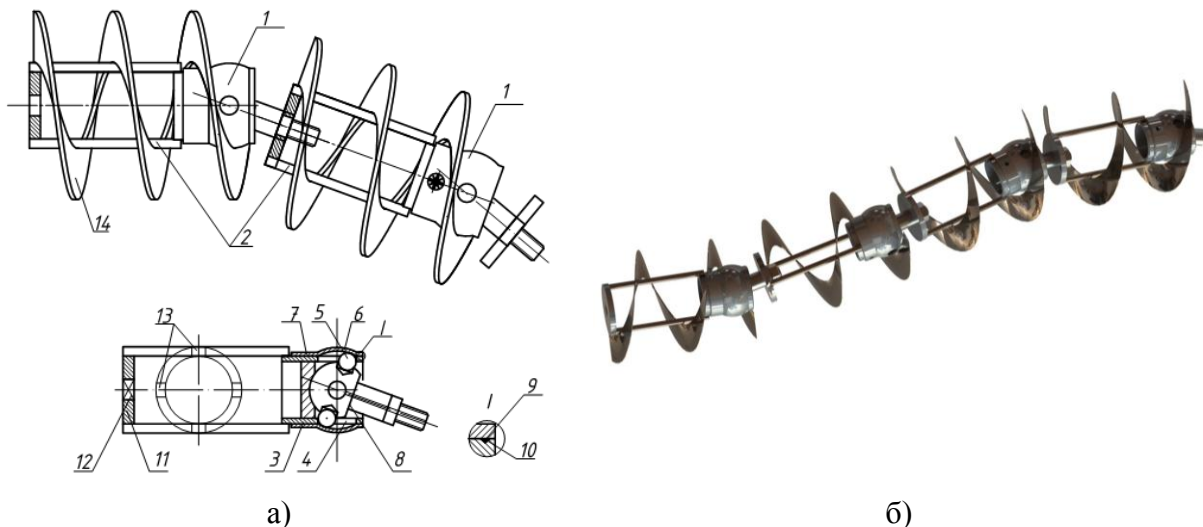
Гвинтовий шарнірно-секційний робочий орган а) конструктивна схема б) загальний вигляд робочого органу
